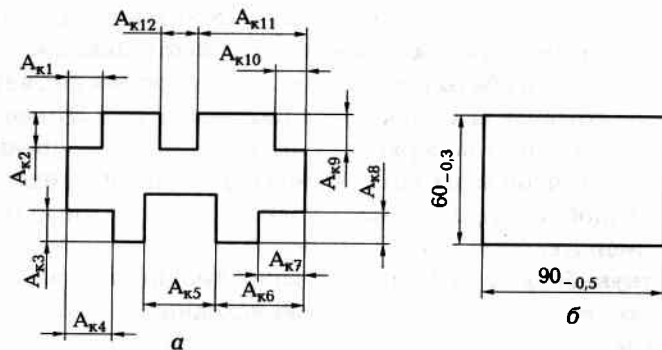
Чертеж обрабатываемой детали (а) и заготовки (б)
